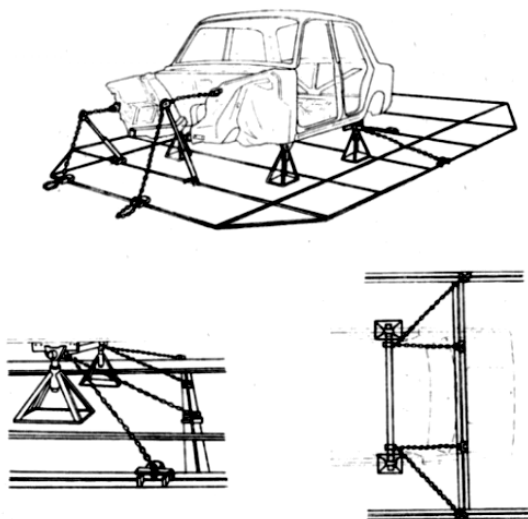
Схема установки и закрепления кузова легкового автомобиля на стенде Р-620 (вверху) и современный напольный стенд «Korek» (снизу)
